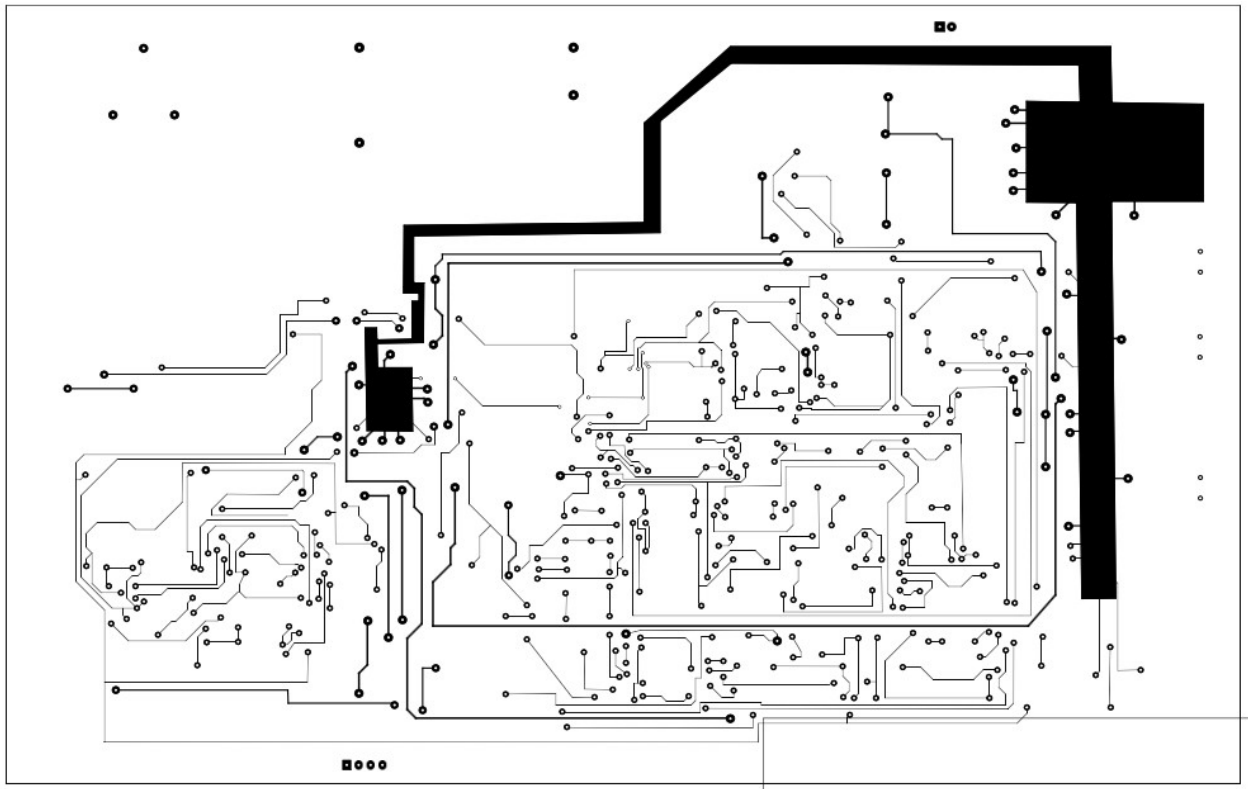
PCB Ki cad del bloque de potencia, capa inferior Bu Cu.
